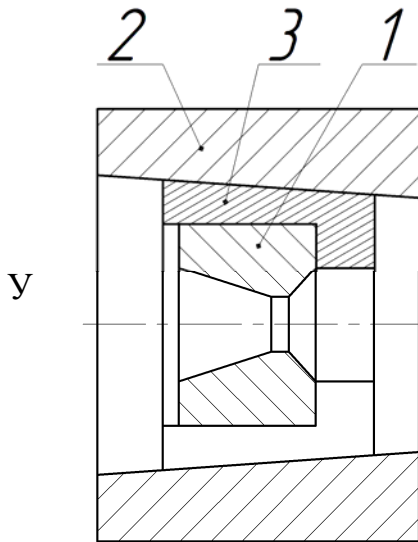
Одинарна волока: 1 - твёрдосплавный вкладыш (волока); 2-стальной корпус; 3 - затисковая втулка (Н.М. Чиглаков)
